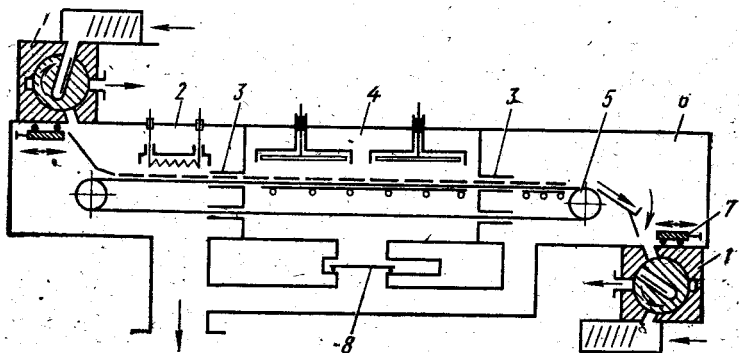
Установка непрерывного действия со шлюзовыми загрузочными устройствами:
